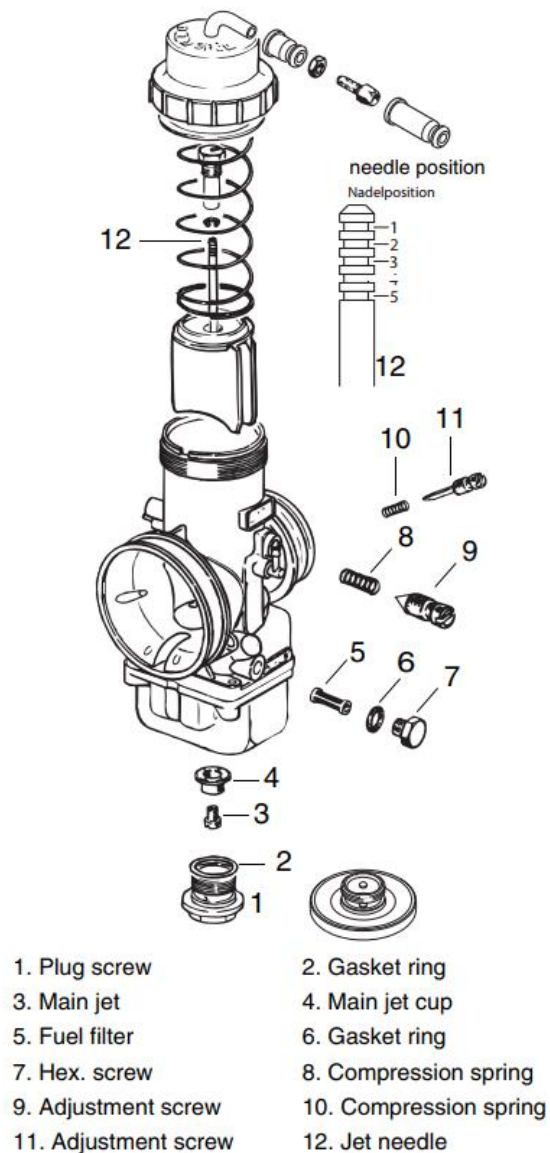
Despiece del carburador Dell'Orto montado en el motor Rotax
